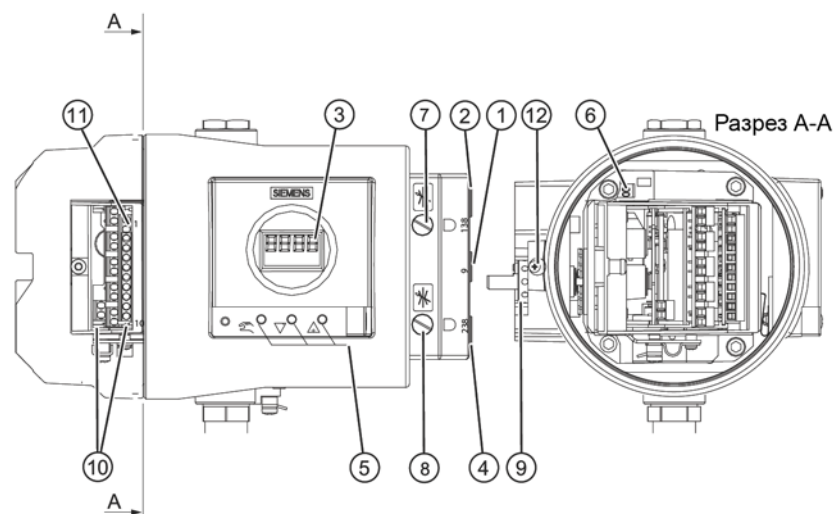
Общий вид позиционера во взрывонепроницаемом корпусе
